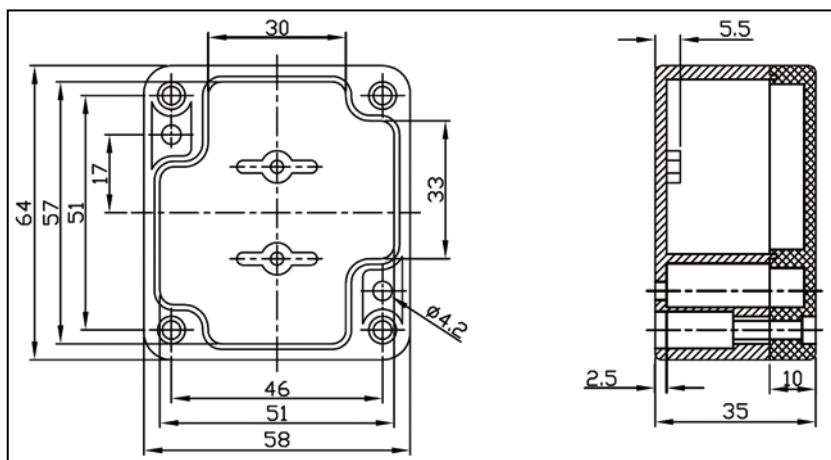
Разветвитель интерфейсный серии ИР. Габаритные размеры корпуса
